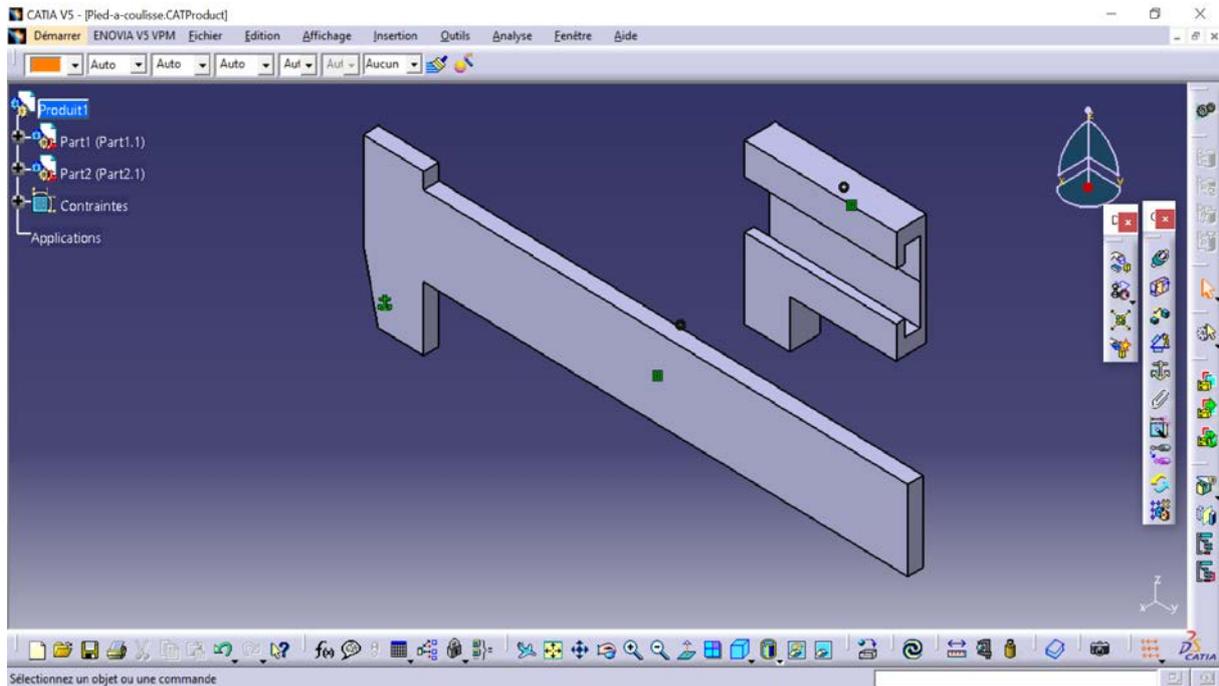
Assembly Design (Insertion du Vernier 2) [1], [2]
